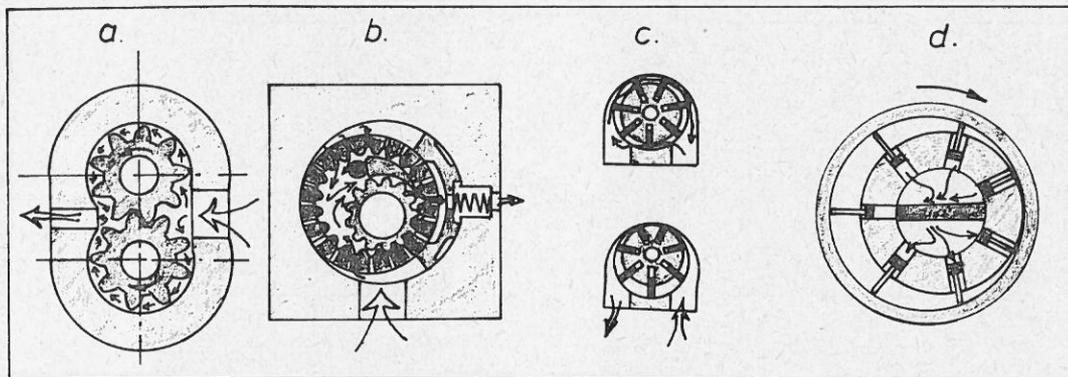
Funktionsweise von Zahnradmaschine (a), Zahnringmaschine (b), Flügelzellenmaschine (c), Radialkolbenmaschine (d).
